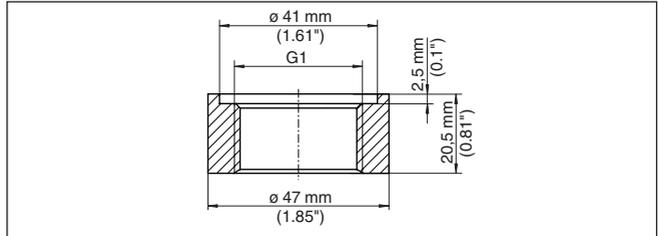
Dimensiones racor para soldar rosca G1 (DIN 3852-X)
